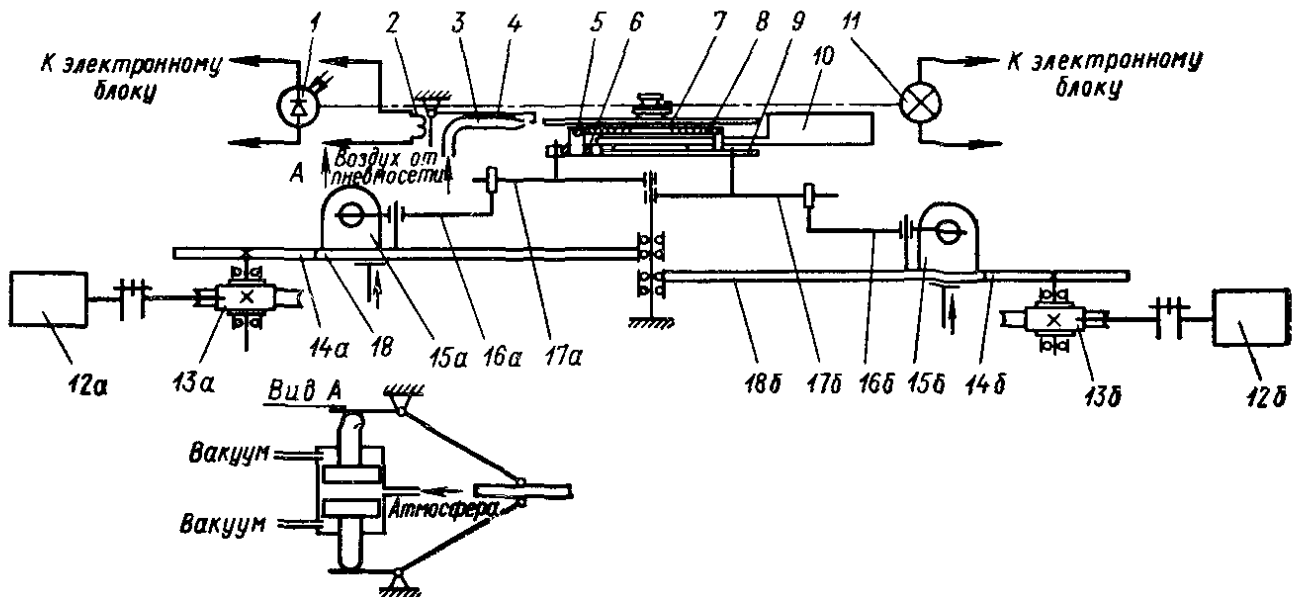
Кинематическая схема прибора для автоматической регулировки периода и положения статического равновесия
